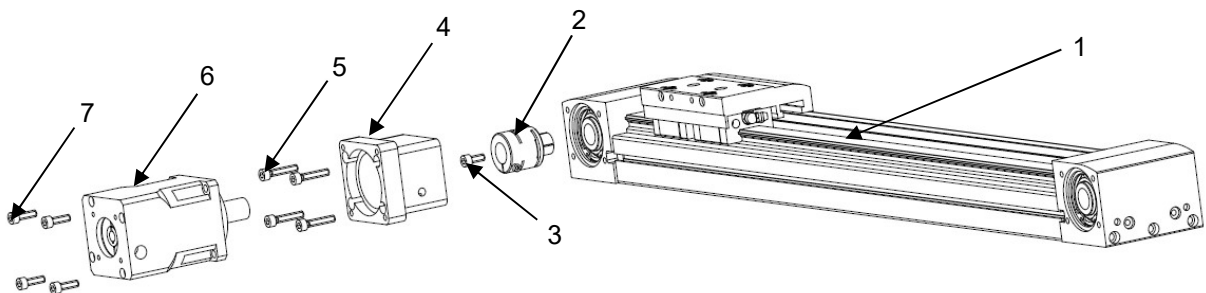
Установка редуктора с помощью монтажного комплекта модели AR-EGT
